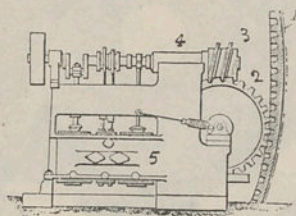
VIRADOR COM MOTOR A VAPOR
